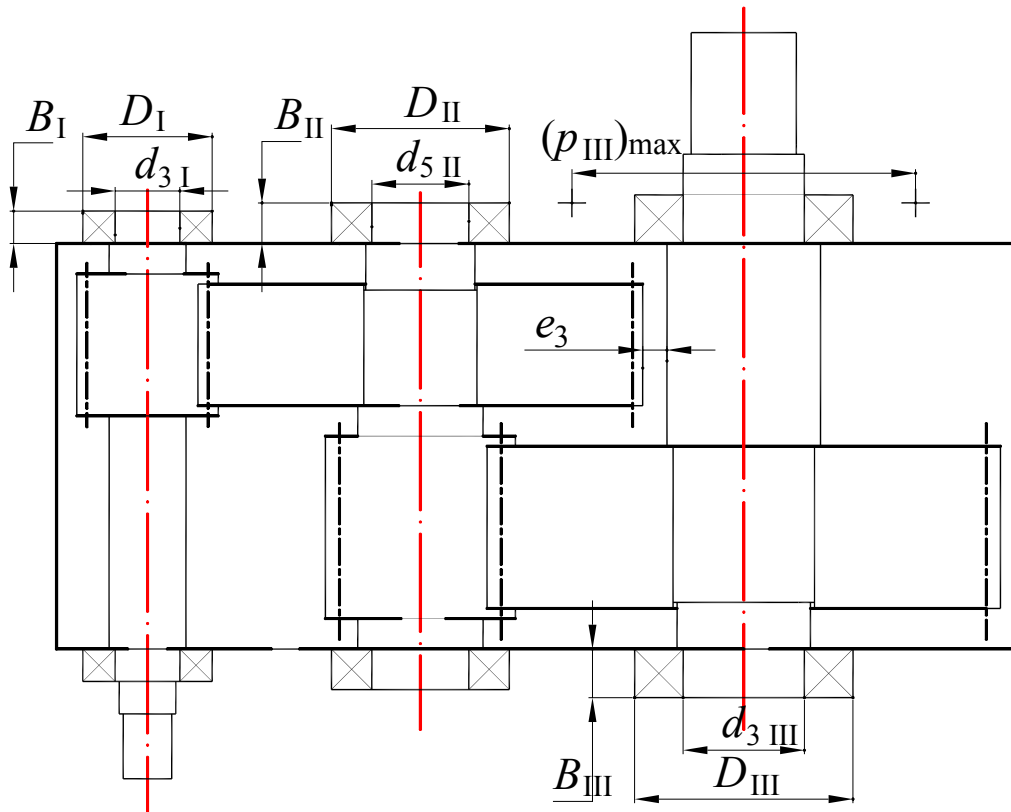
Остаточний результат складання ескісної компоунки циліндричного редуктора за розгорнутою схемою
